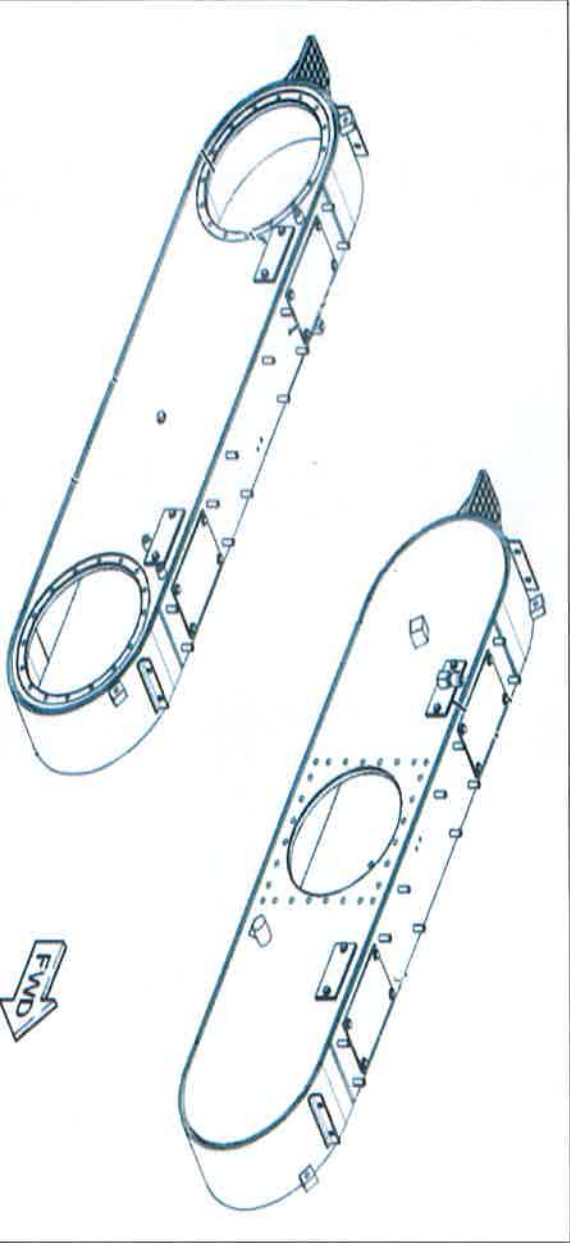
Revisar fisuras, fugas de aceite y daños en la estructura.
